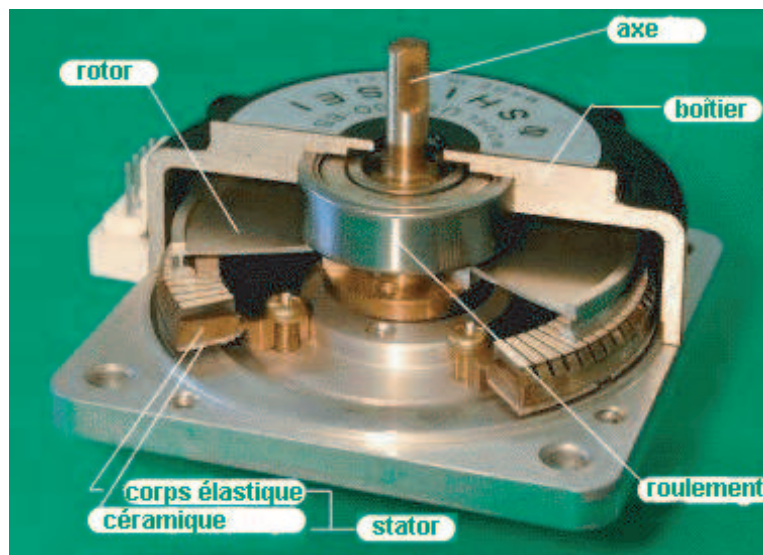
Vue éclatée du moteur SHINSEI USR60.
